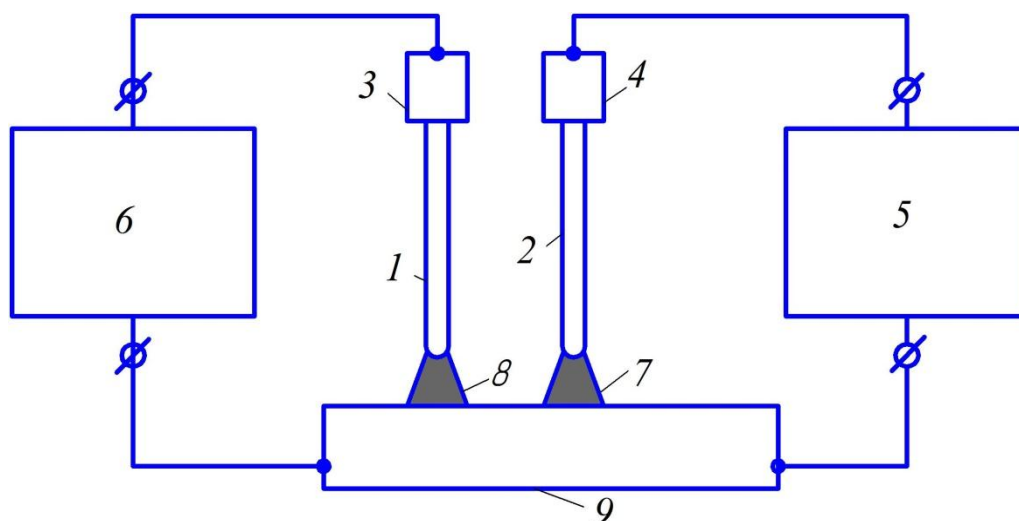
Схема процесса ручной двухдуговой сварки
